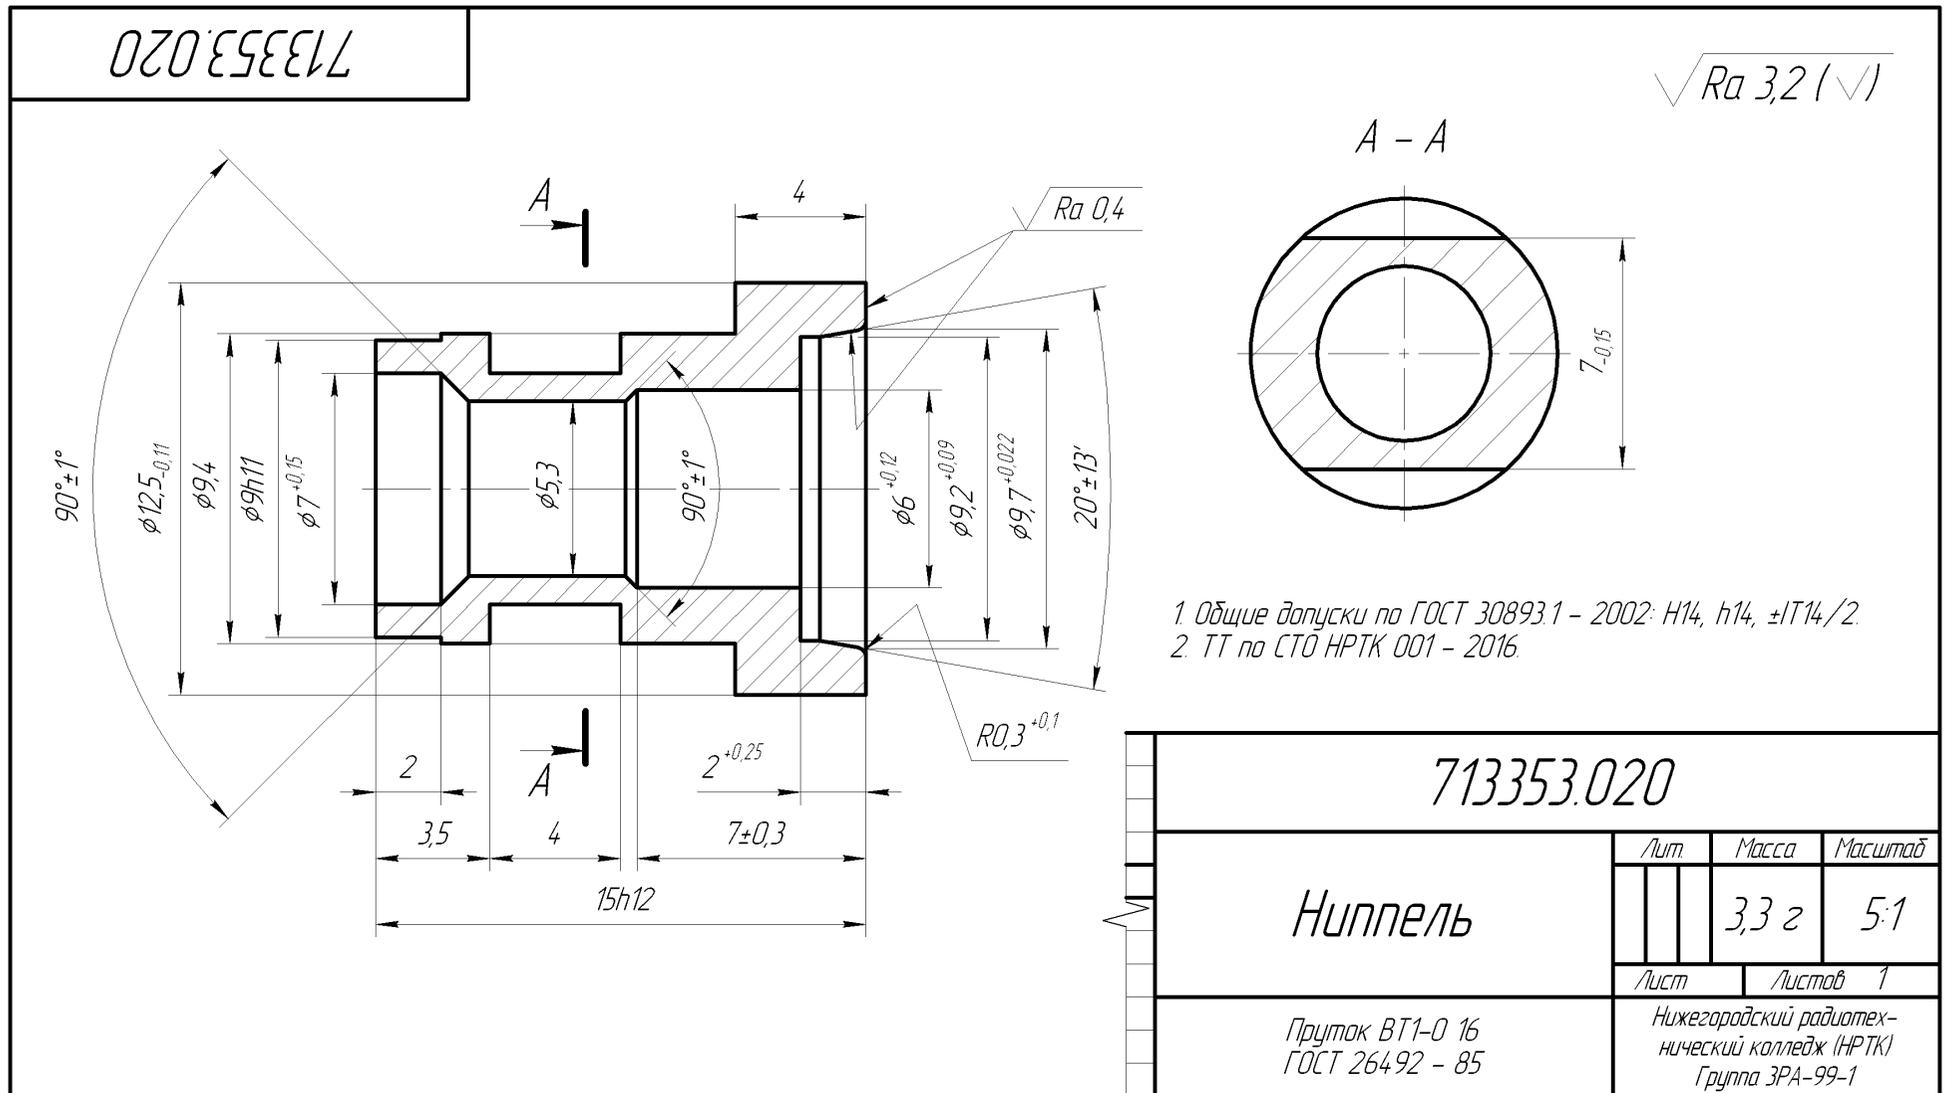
Пример чертежа детали с указанными допусками размеров
